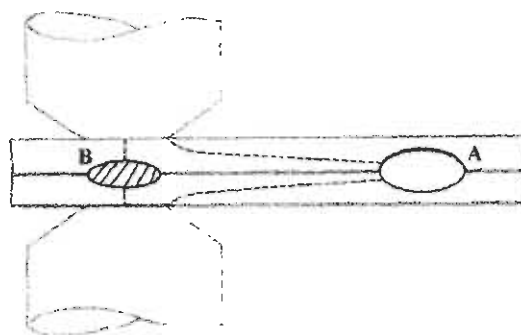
Efecto de desviación entre dos puntos de soldadura. ^[15]
